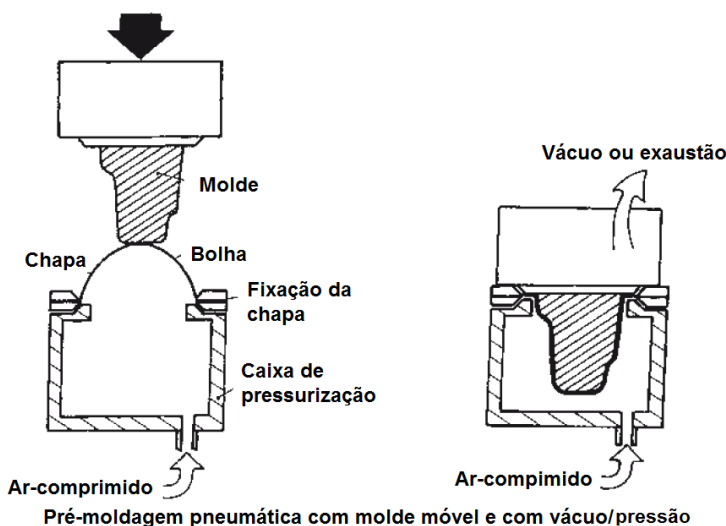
Desenho esquemático exemplificando a pré-moldagem por sopro.
